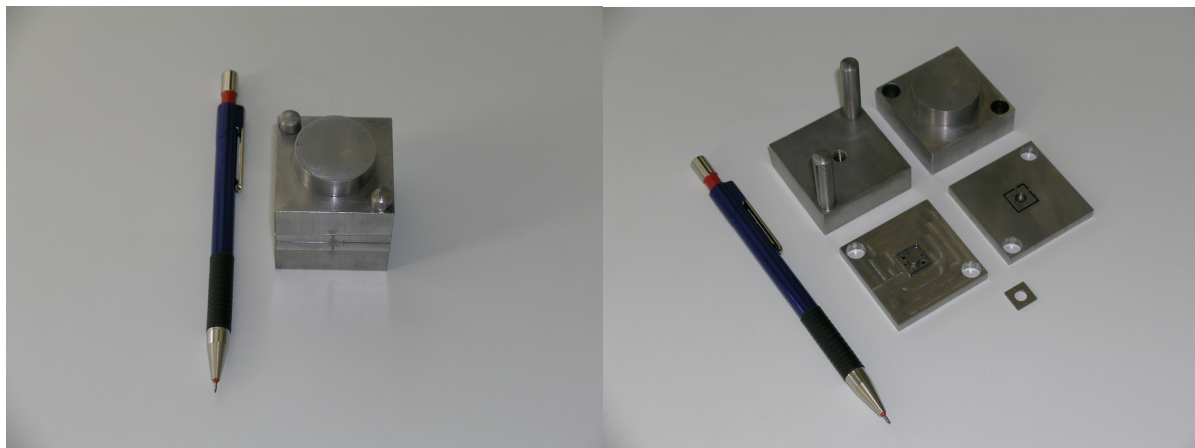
Stanzwerkzeug für PVDF-Folien (links) und seine Komponenten (rechts).
